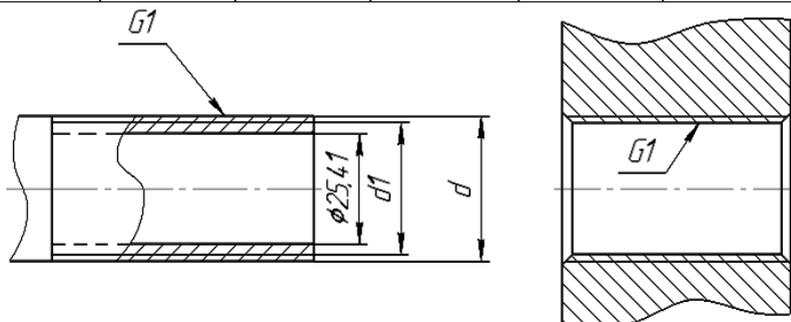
Указание размеров трубной цилиндрической резьбы
